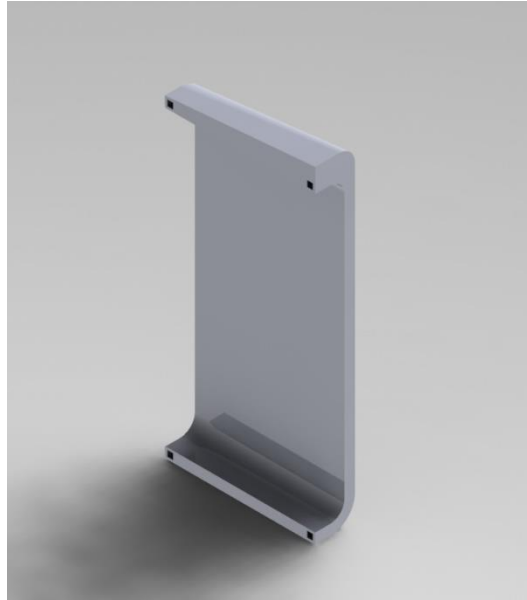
Ensamble subconjunto 1.2. Soldadura 9, 10, 11 y 12.
